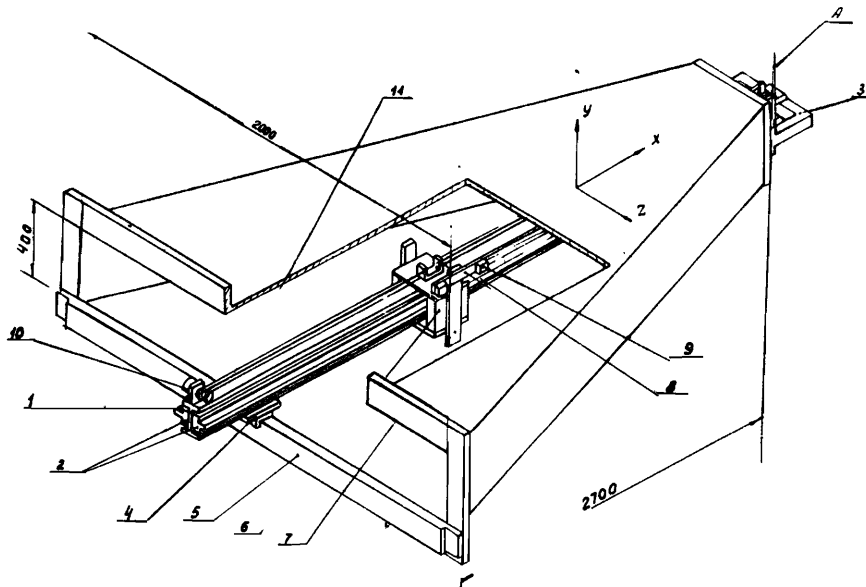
Общий вид камеры и механического приспособления для перемещения датчиков магнитного поля.
